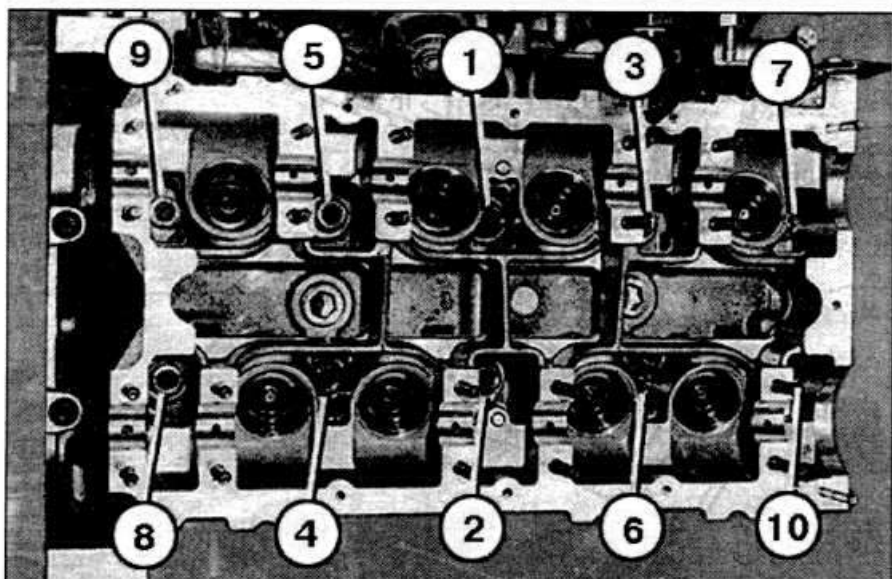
Порядок затяжки болтов крепления головки цилиндров
